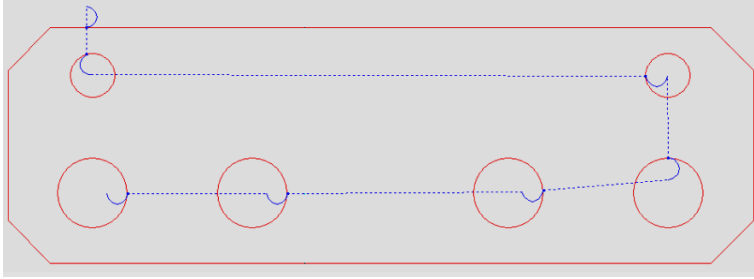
Lazer tezgâhına ait yazılımla minimum kayıpla kesim planının çıkartılması
